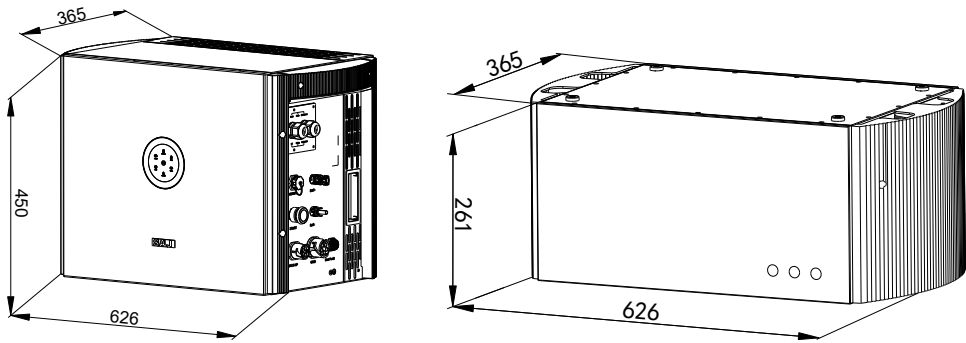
Dimensions du module inverseur et batterie HS2/AS2
